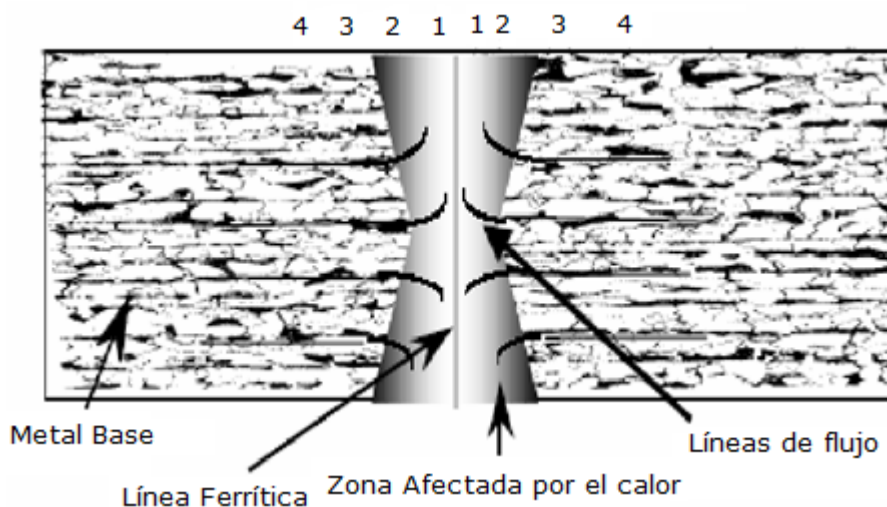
Zonas afectadas producidas por la soldadura ERW. Fuente: Koide, Kondo y Itadani (2006).
